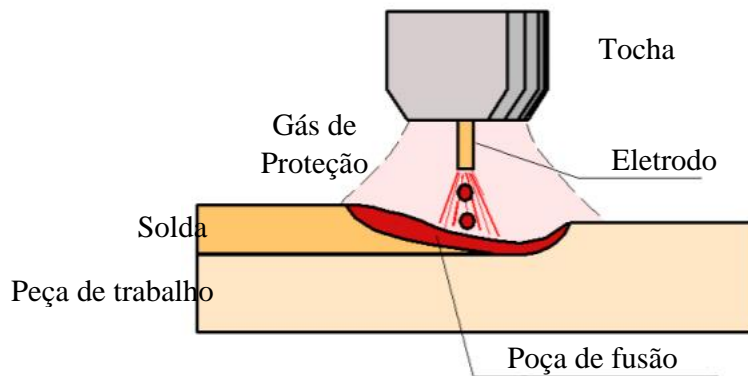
Processo de soldagem GMAW (modificado de Modenesi *et al.*, 2012).
